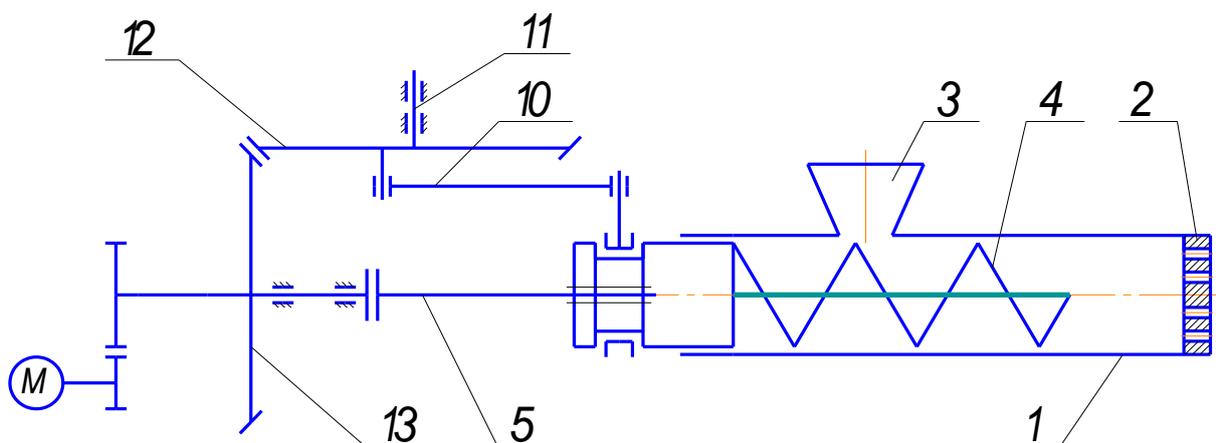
Пресс-экструдер с приводом кривошипа от приводного вала шнека
